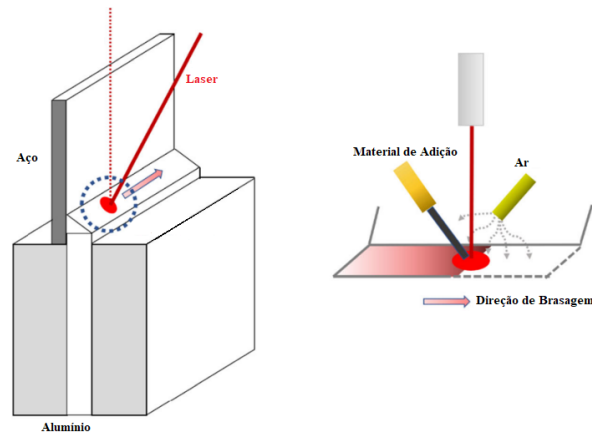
Montagem de Soldadura por Brasagem a Laser, adaptado de [6]
